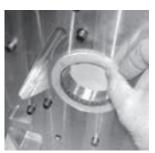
Ziehen Sie die 4 Schrauben an, während Sie die Auslöserbaugruppe in Ihrer Position halten.
